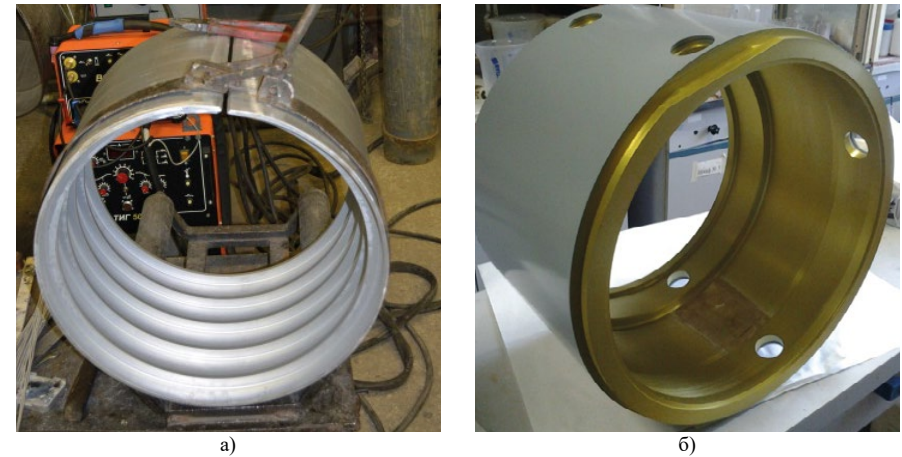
Корпуса из новых алюминиевых сплавов: а) сварка корпуса из сплава 1575-1; б) корпус из сплава 1933Т33 для натурных коррозионных испытаний
